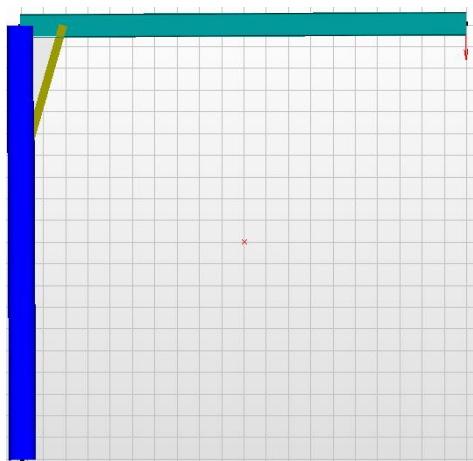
Общий вид крана на колонне и расчетная схема
